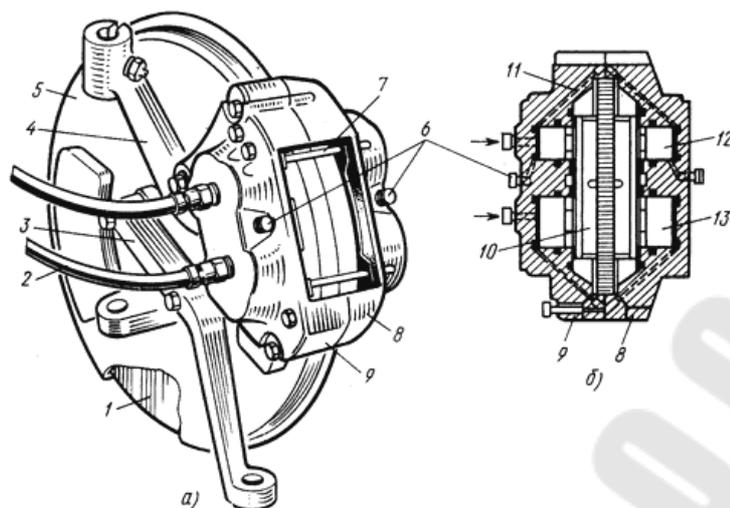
Колесный дисковый тормозной механизм:
